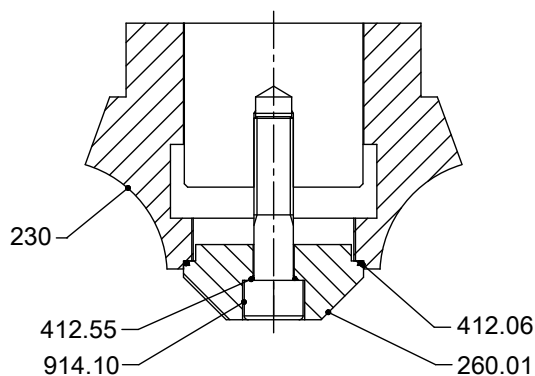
Laufradbefestigung M100 × 2 (für die Hydraulik K 500-632, K 500-640)
